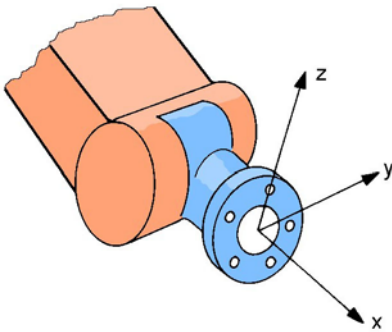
Flansch- bzw. Werkzeugkoordinatensystem
